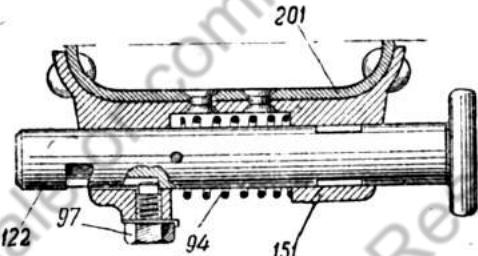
Стопор крепления по-походному подъёмного механизма (сб. 03):
